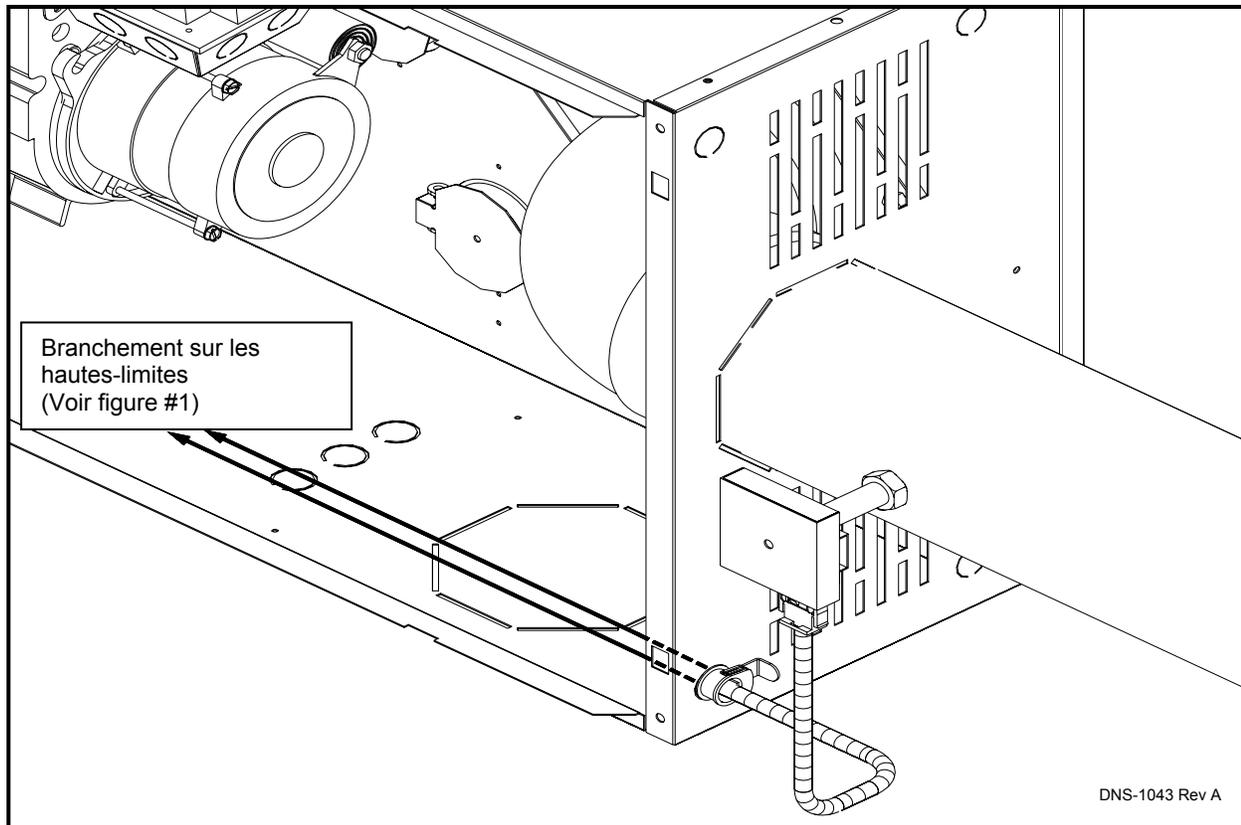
Arrangement général du système anti-refoulement, installation en débit d'air horizontal et évacuation verticale
